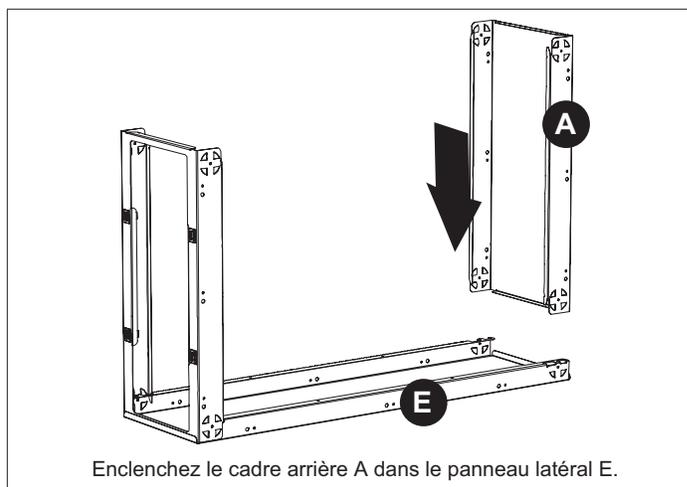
Assembler le cadre arrière (A) dans le panneau latéral (E)
